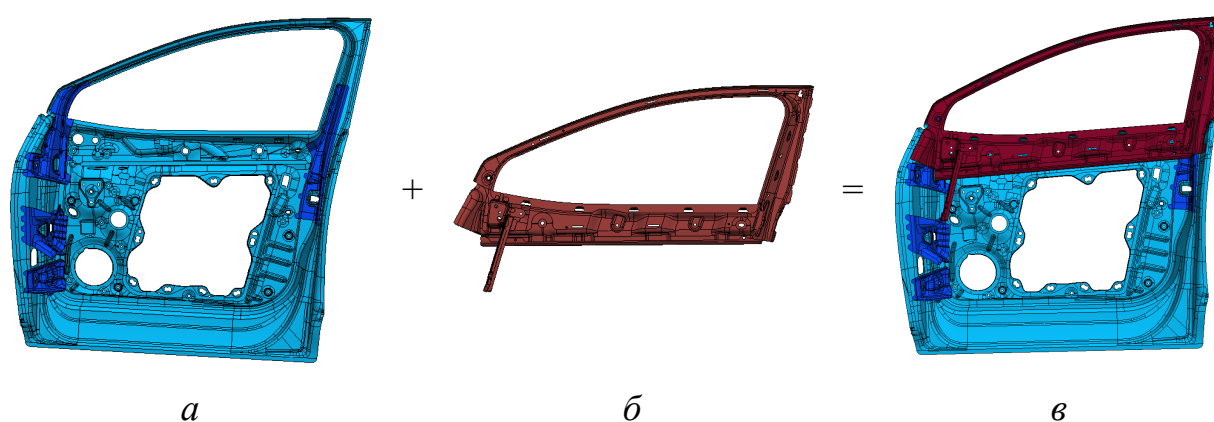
Схема сборки автодетали на проектируемом участке цеха
